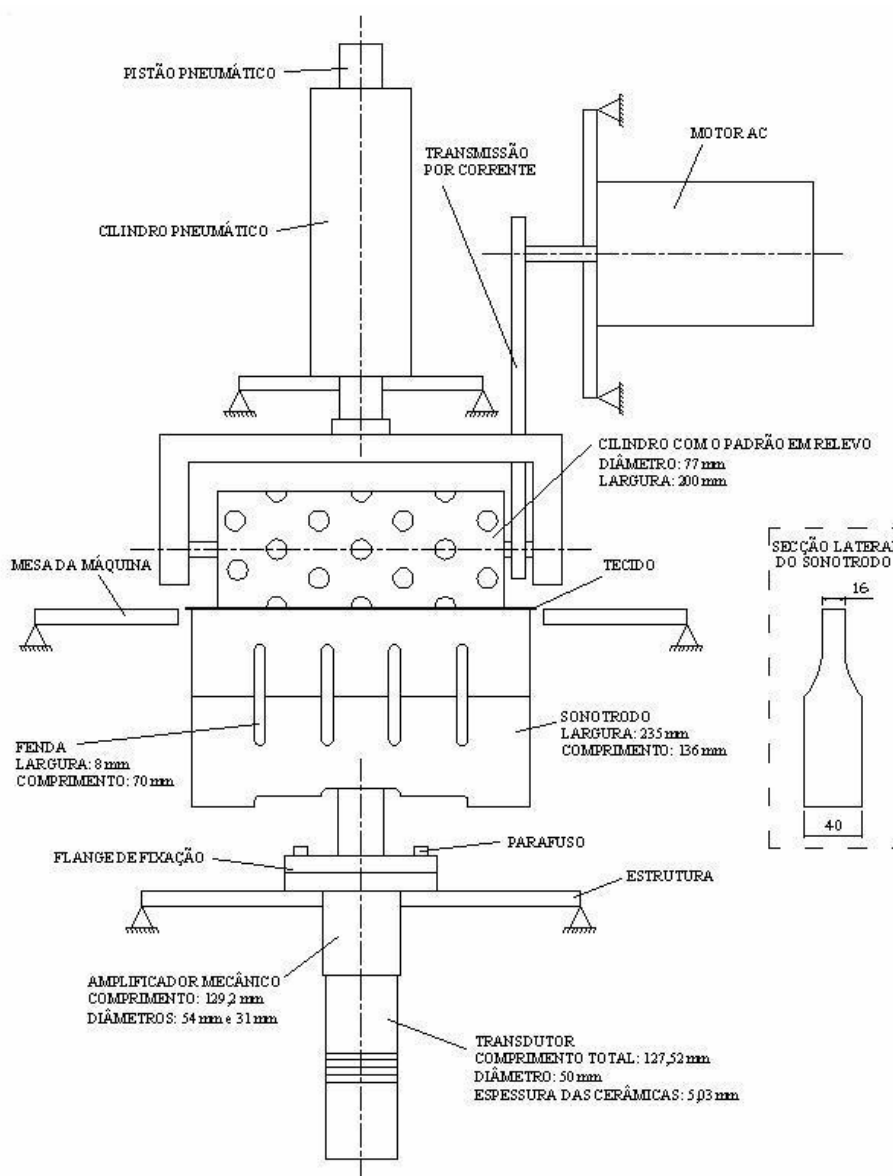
Representação esquemática do processo de corte e soldagem de tecidos sintéticos por ultra-som.
